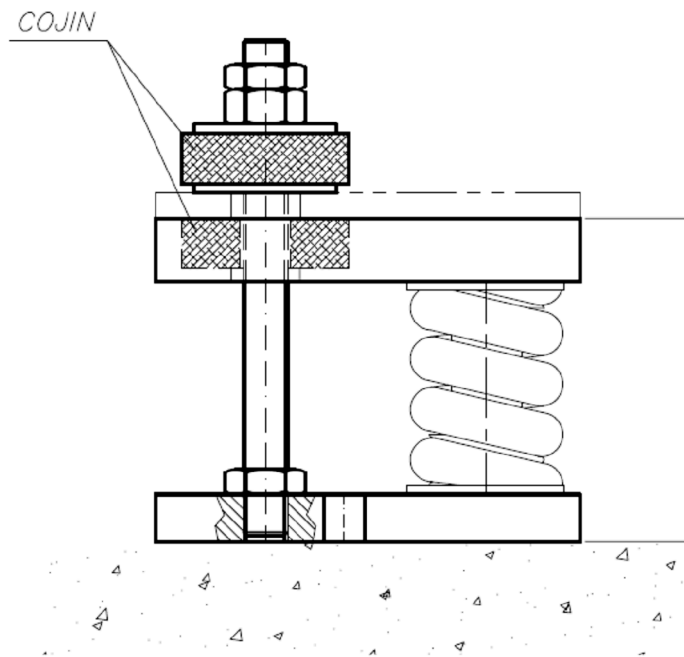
ó Plano amortiguador proyecto real 3. Vista en alzado
